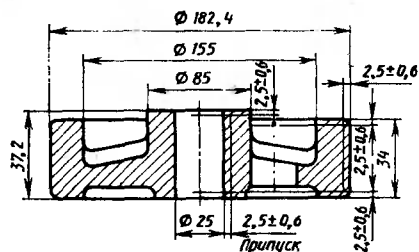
Заготовка зубчатого колеса из серого чугуна
